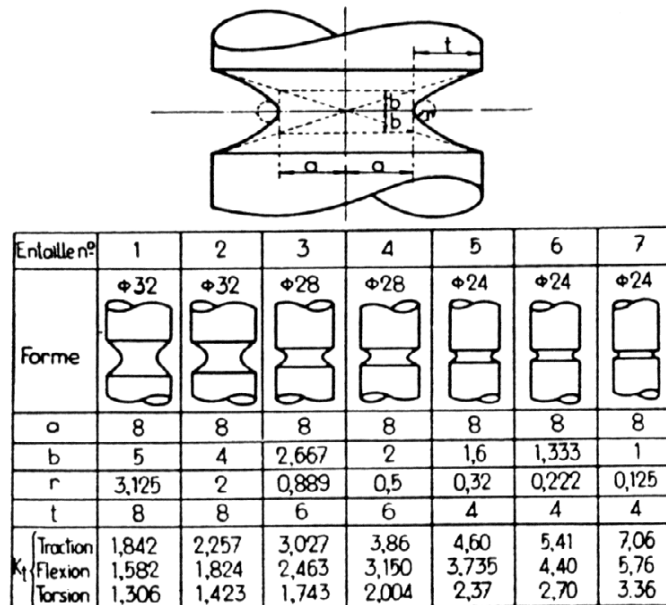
Définition géométrique des entailles usinées des éprouvettes de Massonnet (extrait de [68]).
